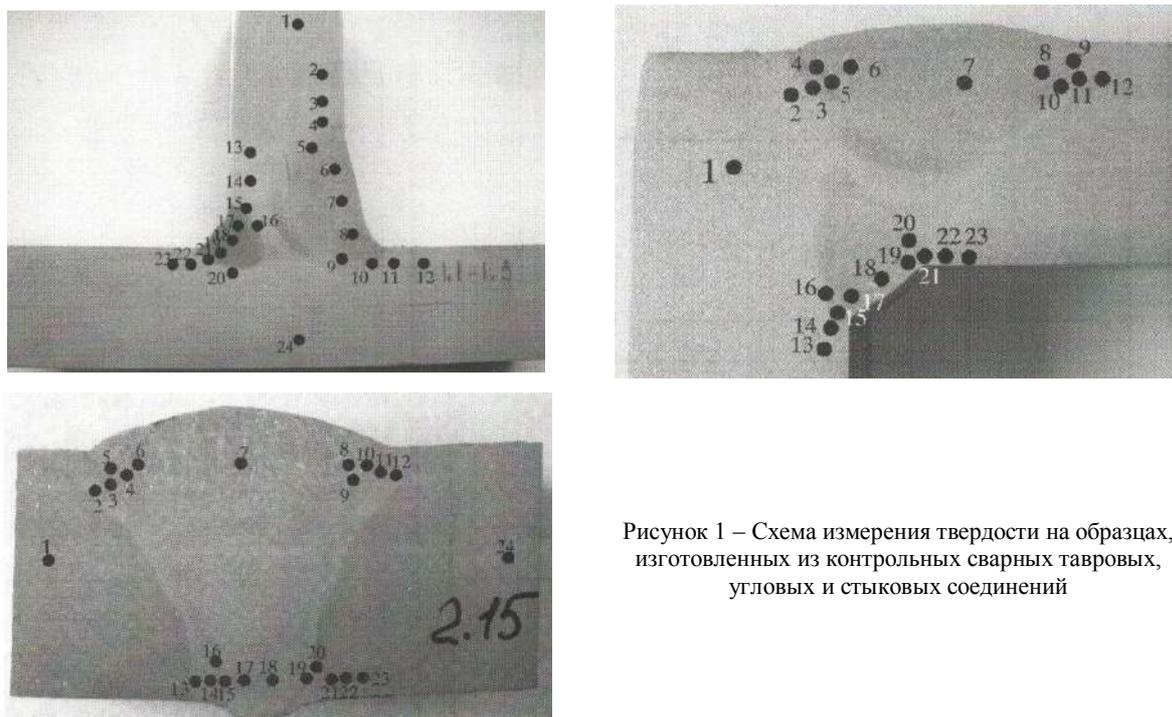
Схема измерения твердости на образцах, изготовленных из контрольных сварных тавровых, угловых и стыковых соединений
